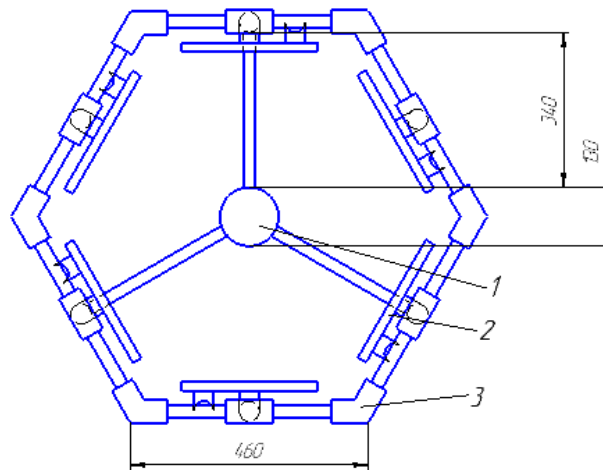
Вид сверху лабораторного стенда: 1 – источник излучения; 2 – солнечный модуль; 3 – каркас
